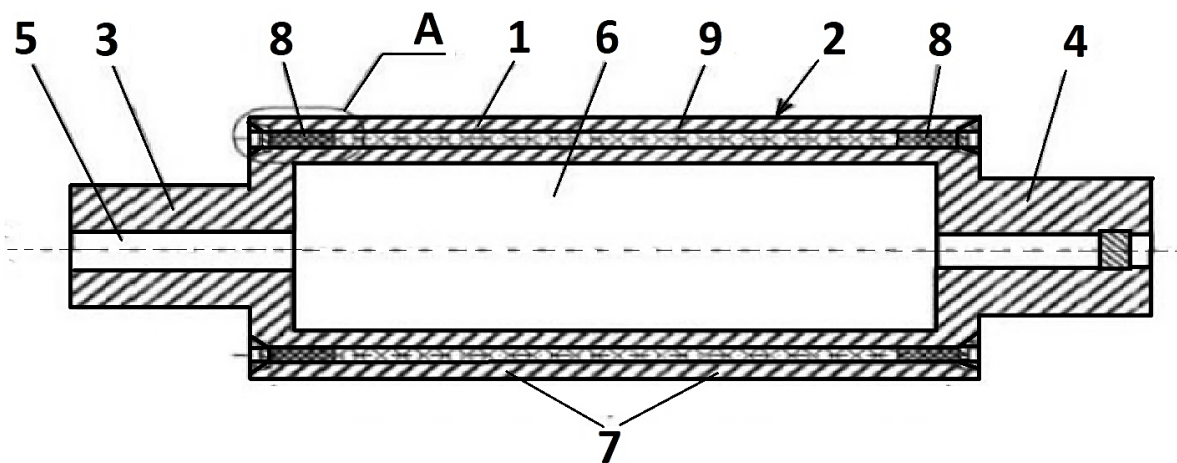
Валок машини Поздовжній розріз валка: 1 – циліндр, 2 – робоча поверхня з нанесеними пазами, 3,4 – цапфи, 5 – центральний канал для валу, 6 – порожнина, 7 – пази каналу, 8 – кінцеві ділянки, 9 – середня ділянка
